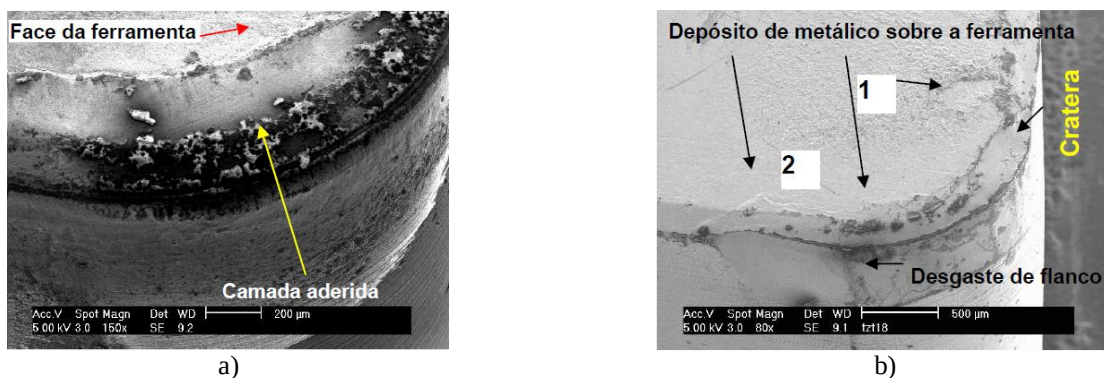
Caracterização do desgaste da ferramenta: a) Usinagem do FC com Si_3N_4 não revestido e b) Usinagem do FV com Si_3N_4 não revestido.
